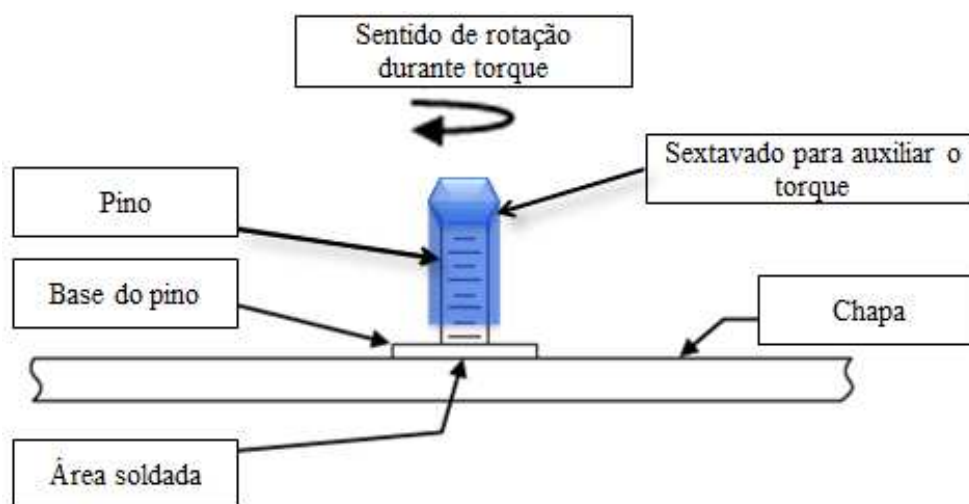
Esquema do ensaio de torque realizado no conjunto soldado Pino/Chapa
